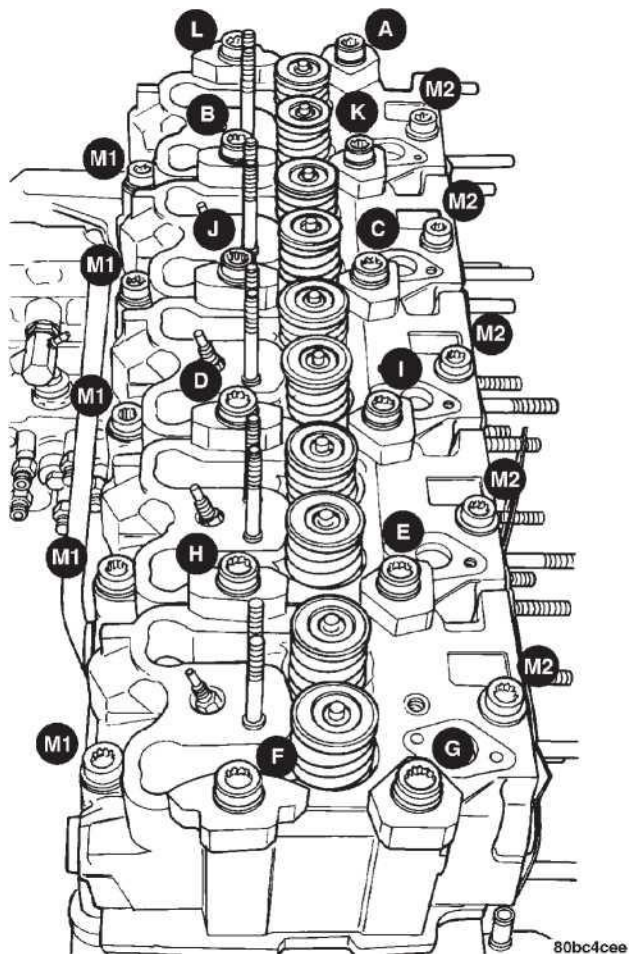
Последовательность затяжки болтов головки цилиндра двигателя
